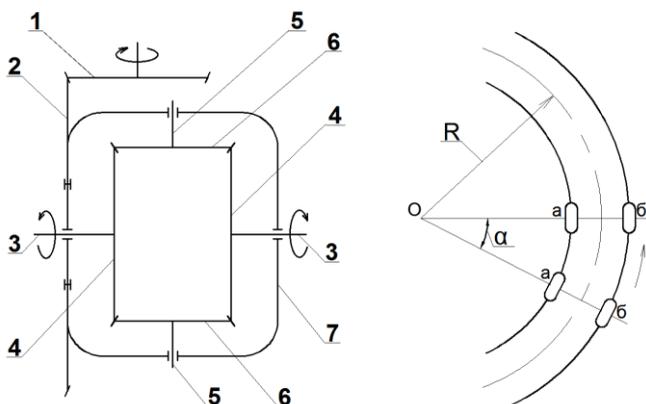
Схема главной передачи и дифференциала и траектория движения колес автомобиля на повороте:
